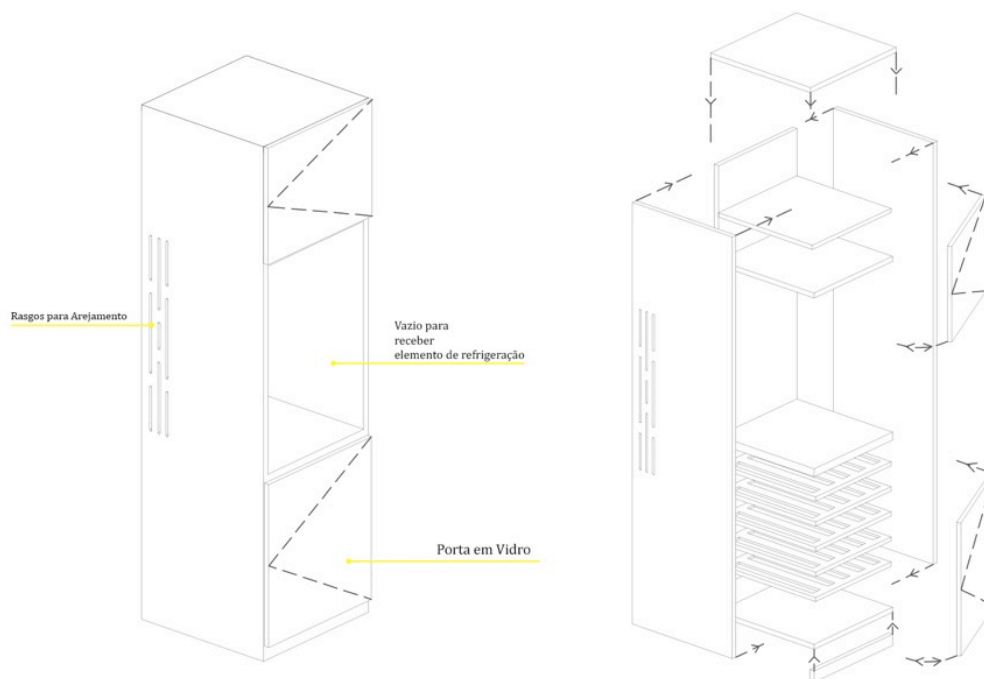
Desenho técnico de execução do equipamento, Axonometria de conjunto e explodida
